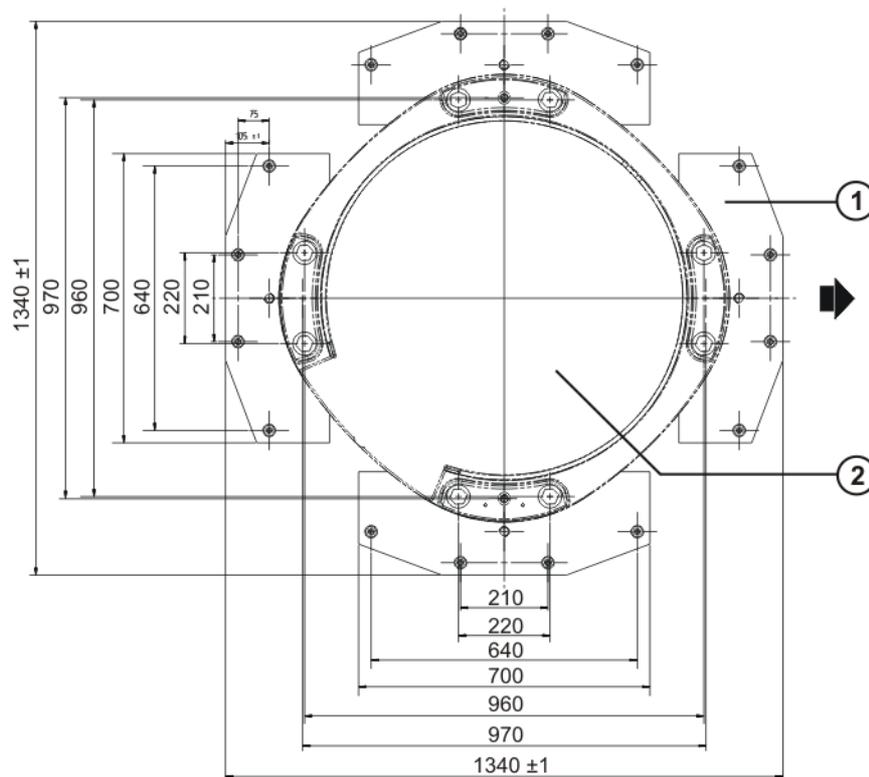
Fixation aux fondations, 200 mm, plan côté
